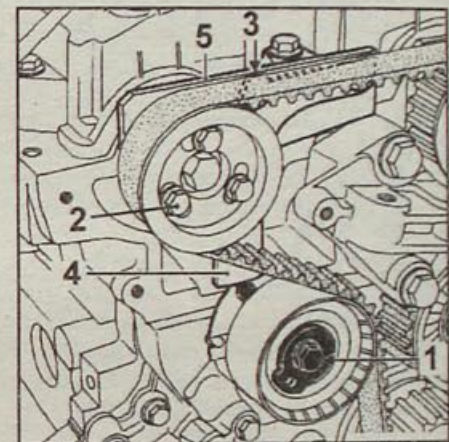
Регулировка натяжения ремня привода газораспределительного механизма:
